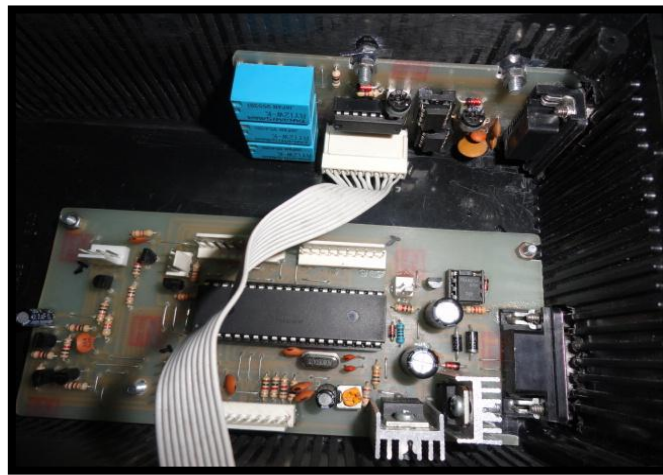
Soldadura de cada arnés con su respectivo conector MOLEX.
